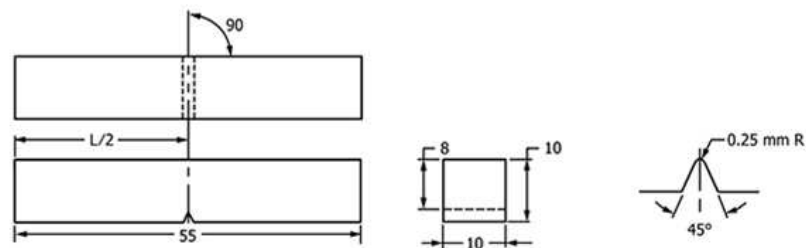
Dimensiones de la probeta para ensayo de impacto Charpy de acuerdo con la norma ASTM E23 [39].
